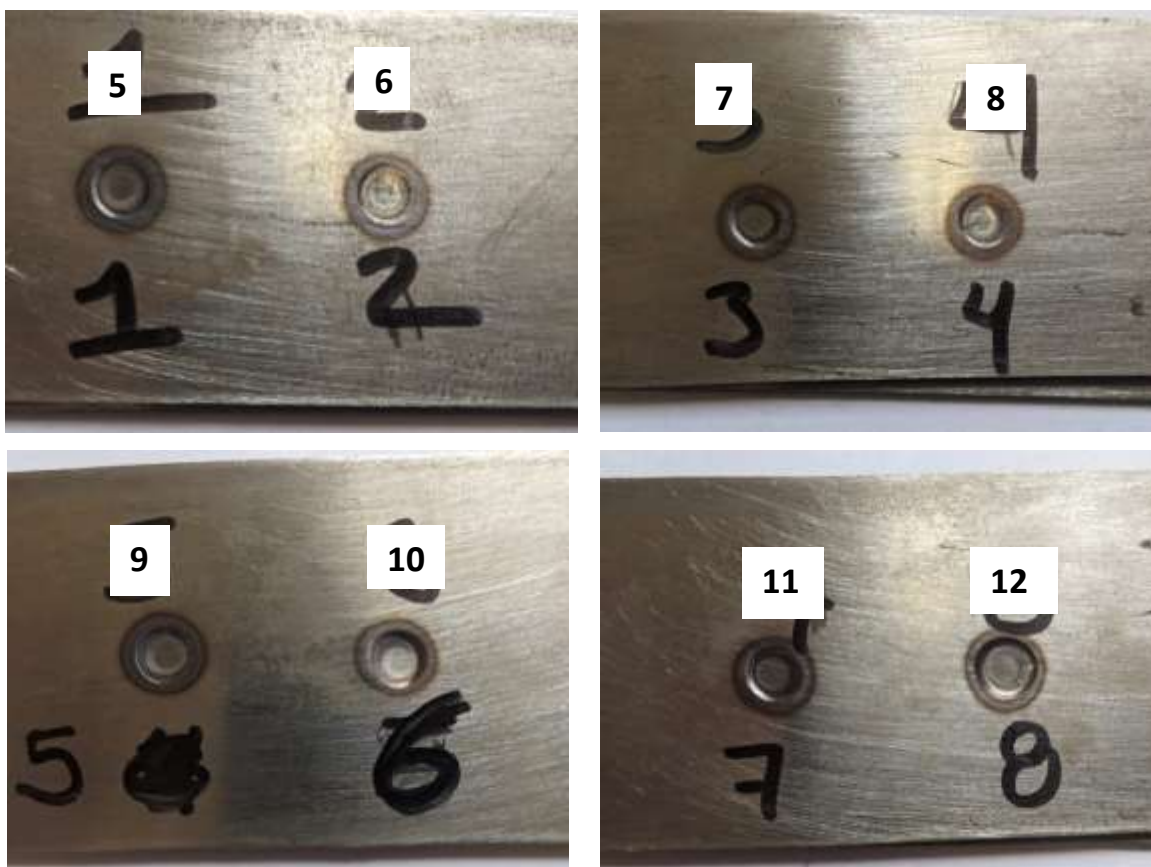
Botones de soldadura obtenidos en el segundo grupo de pruebas.
